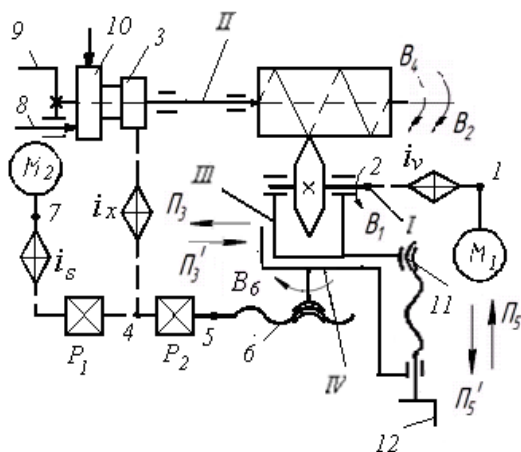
Кинематическая структура резьбофрезерного станка с механическими связями
